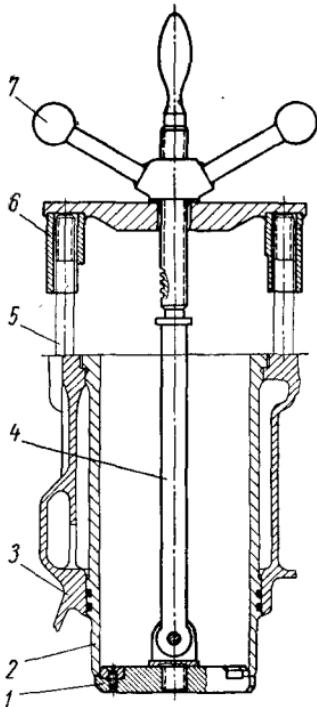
Приспособление для съема гильзы из блока цилиндров:
